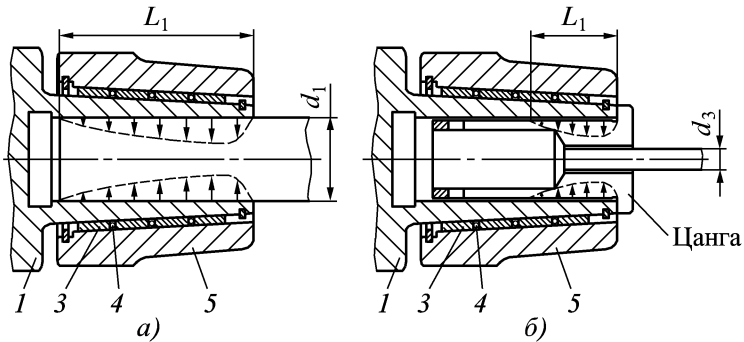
Деформация корпуса (а) роликового патрона и закрепленной в нем цилиндрической цанги (б): обозначения см. рис. 39
